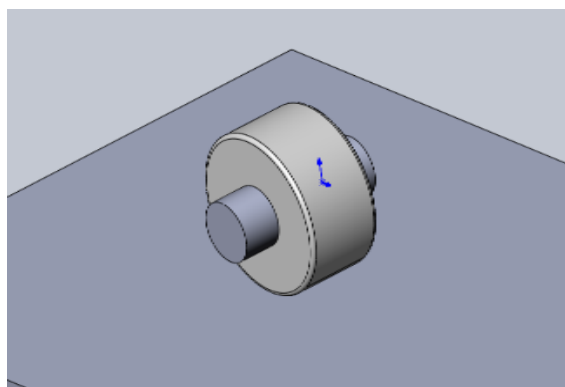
Модель выглаживающего инструмента в форме цилиндрика
